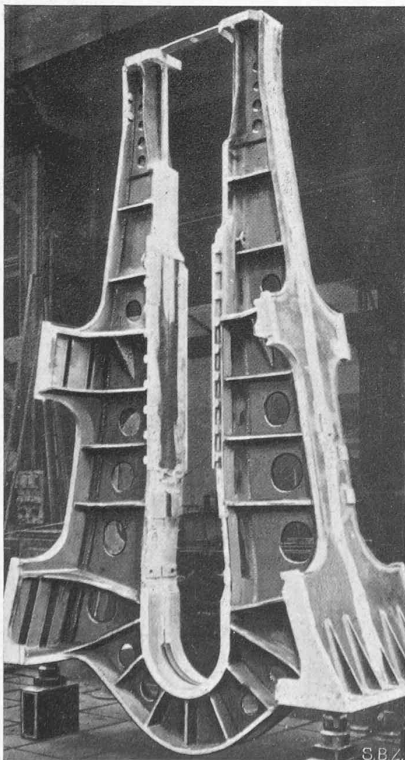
Geschweisster Rahmen zum Motor Abb. 5.
